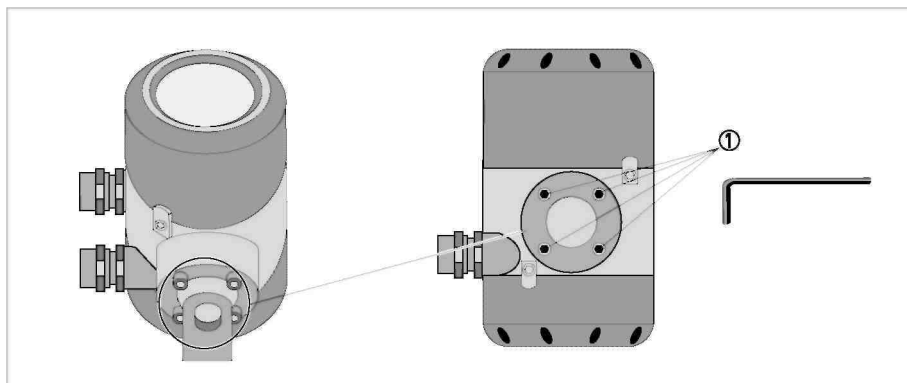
Установочные винты на корпусе соединительного гнезда
